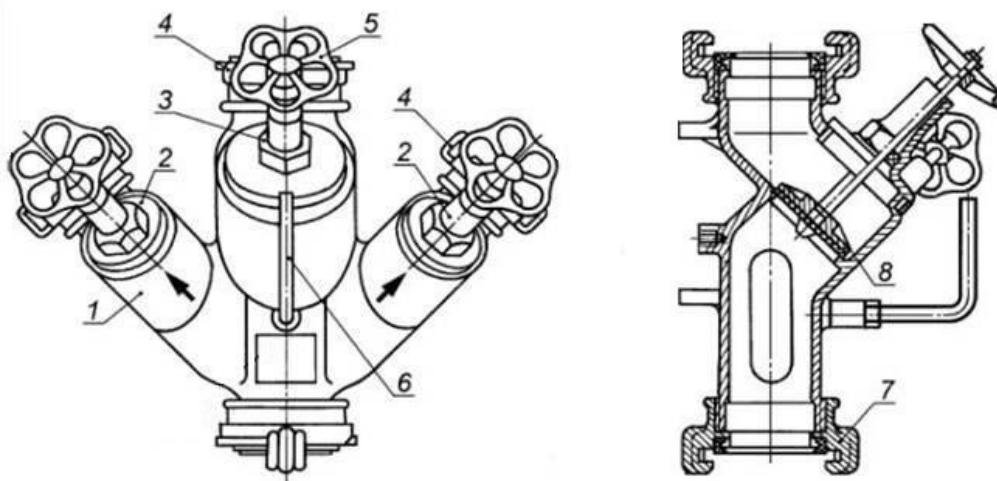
Розгалуження рукавне РТ-70: 1 — корпус, 2 — пристрій перекривання бічного вихідного патрубка, 3 — пристрій перекривання центрального вихідного патрубка, 4 — сполучна головка на вихідному патрубку, 5 — маховик, 6 — ручка, 7 — сполучна головка на вхідному патрубку, 8 — затворний клапан
